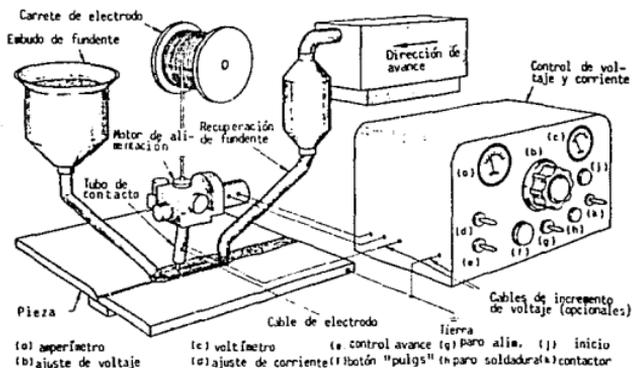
Componentes esenciales de una máquina típica para soldadura automática por arco sumergido.
